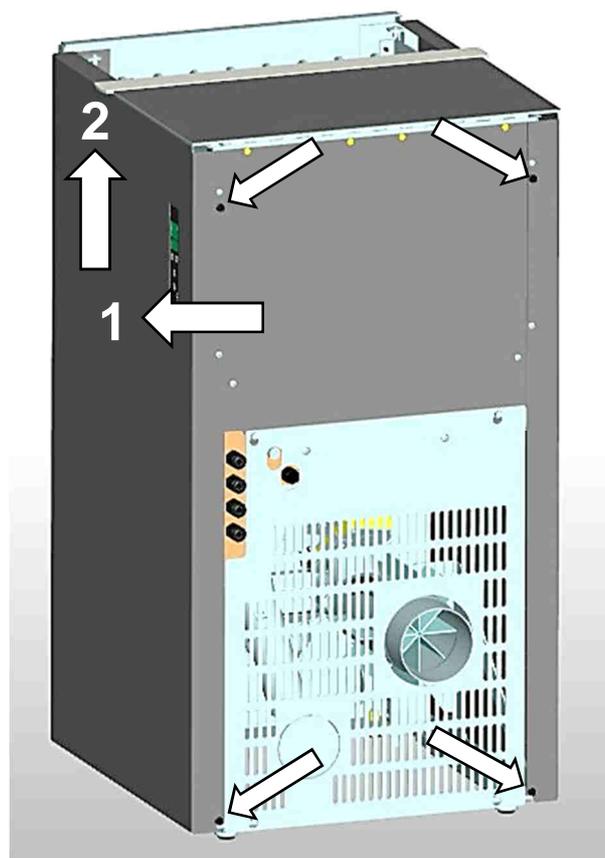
vis du panneau arrière Pat/Pat selection eq
